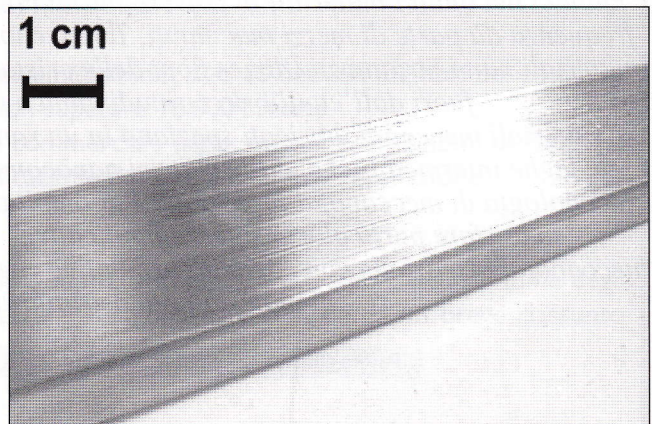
Esempio di estruso diretto da polveri di lega Mg-Li (Mechanomade M 901) nanostrutturata- barra di sezione rettangolare 35x10 mm
